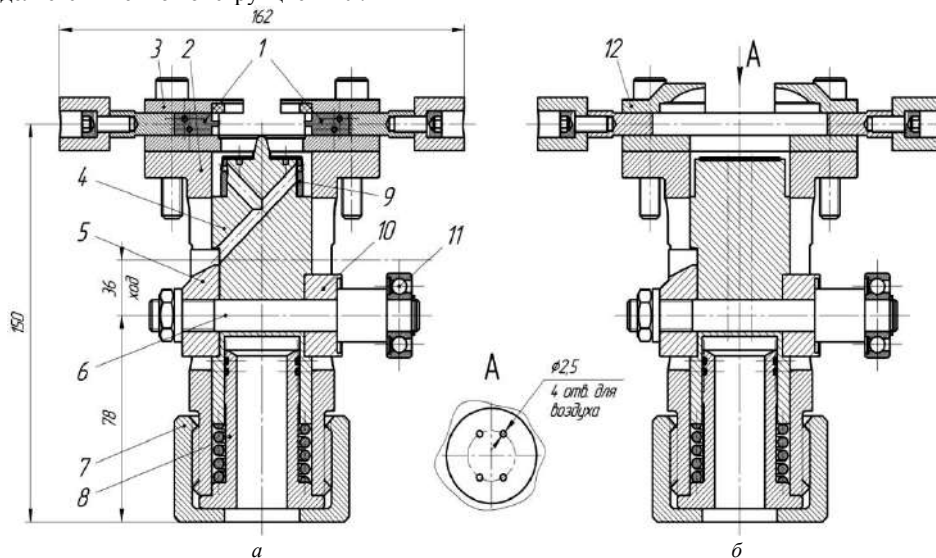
Эскиз ПУ для изготовления мембран гранаты 7П39 (а) и предохранительной мембраны МР-5 (б): 1 – пуансоны пробивки; 2 – корпус; 3 – накладка; 4 – опора; 5, 10 – направляющие; 6 – ось; 7 – гайка; 8 – шток; 9 – матрица пробивки; 11 – подшипник; 12 – полуматрица вытяжки под давлением
